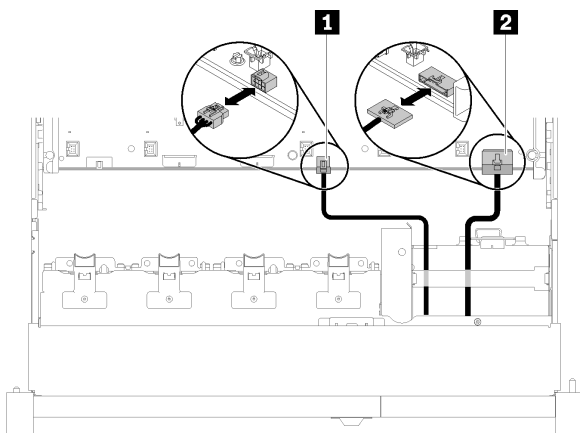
Cabo USB 2.0 e cabo do painel frontal do operador
